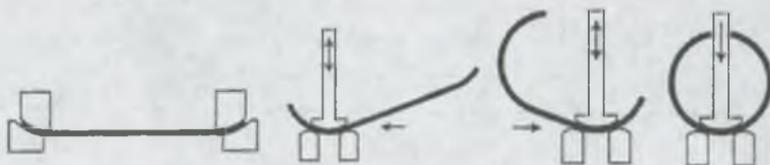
Схема пошаговой формовки трубной заготовки для прямошовных труб.
